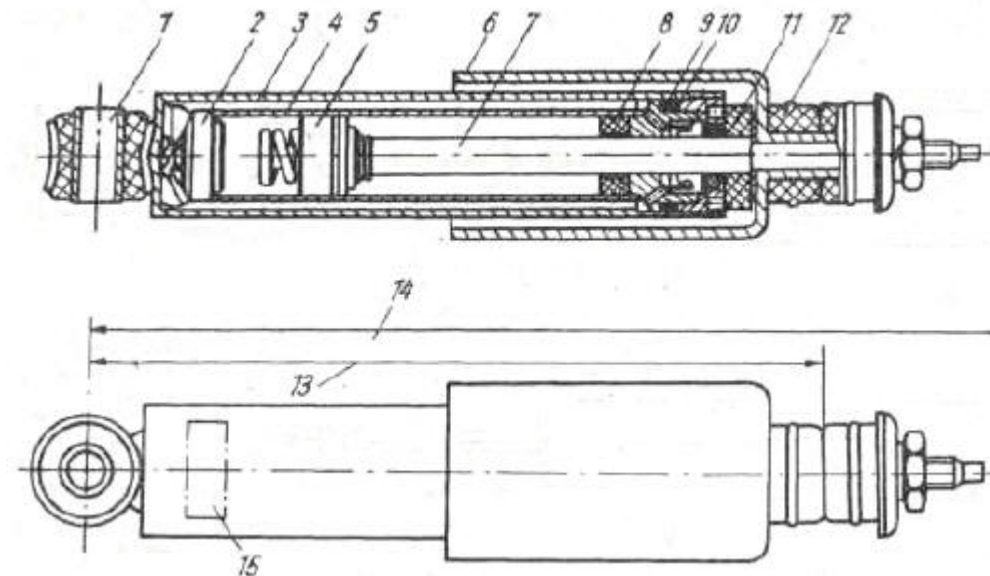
Teleskop-Schwingungsdämpfer (29)
